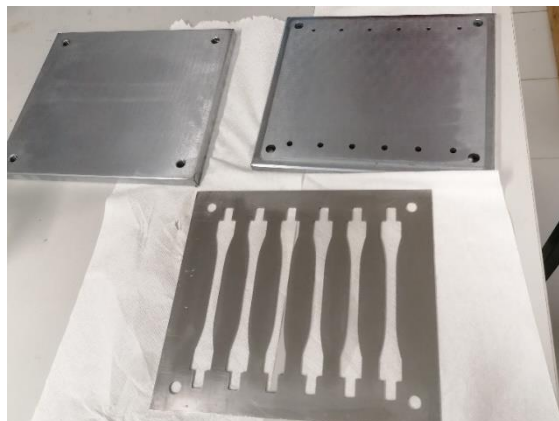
Molde para fabrico dos provetes de adesivo maciço.
